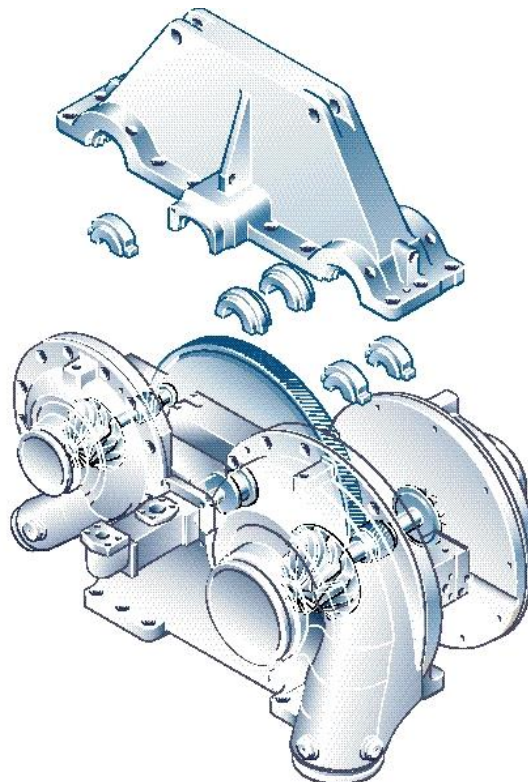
Основные элементы конструкции двухвального трехступенчатого компрессора ряда ZH 4000 – 7000 Atlas Copco
